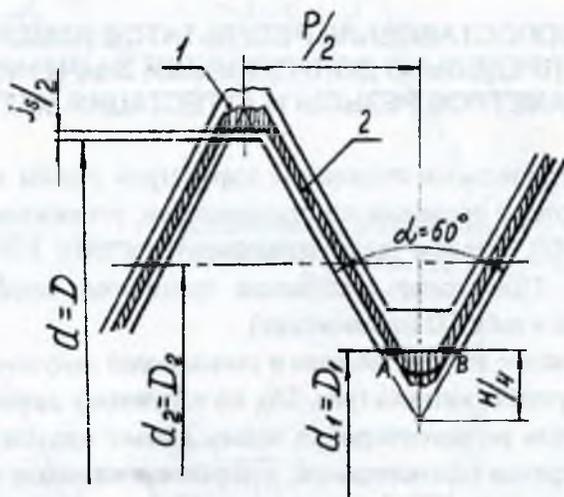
Схемы полей допусков нарезаемой резьбы и резьбы метчика:
